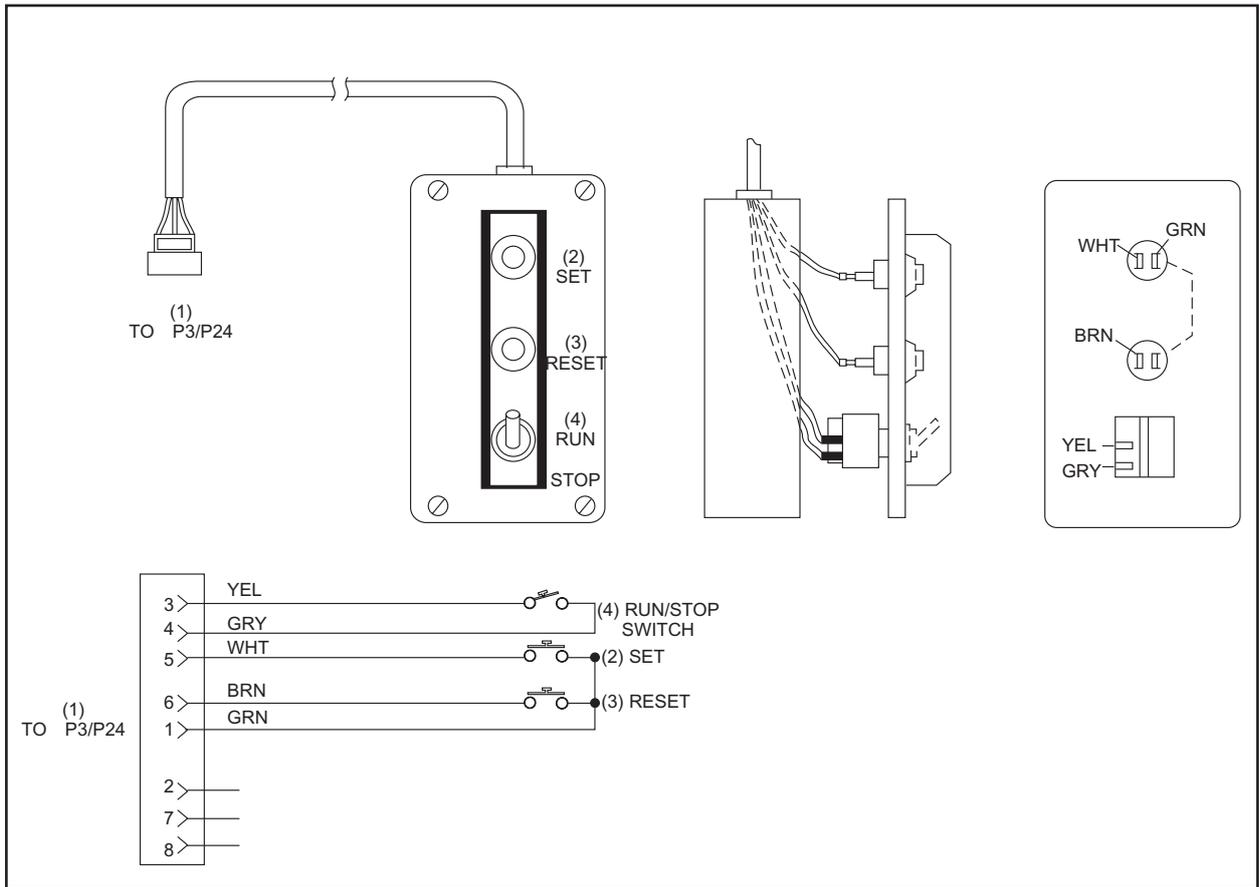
Ensemble câble boîtier de contrôle arrière (Pièce N° 47-245422-003)
